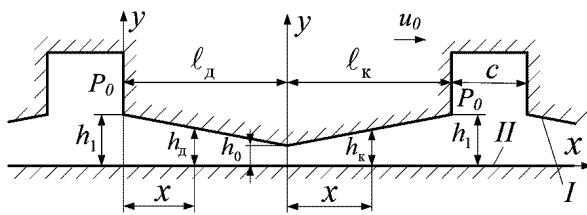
Розгортка поверхнь з конфузорно-дифузорними каналами
